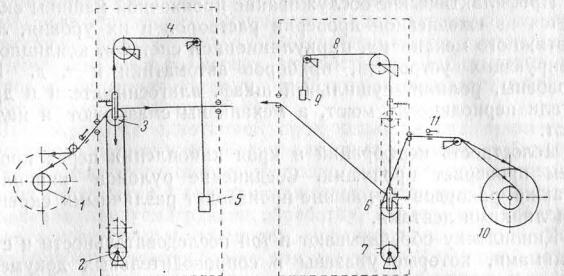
Схема загрузочного и разгрузочного магазинов:
